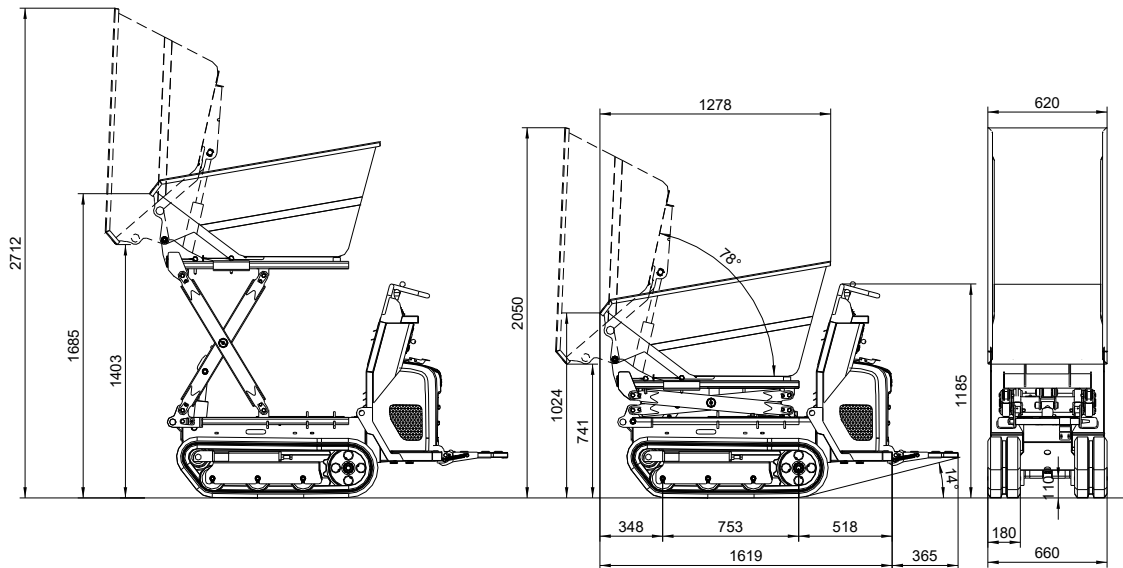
Dimensions de la machine (modèle DT05-D avec benne surélevée)
